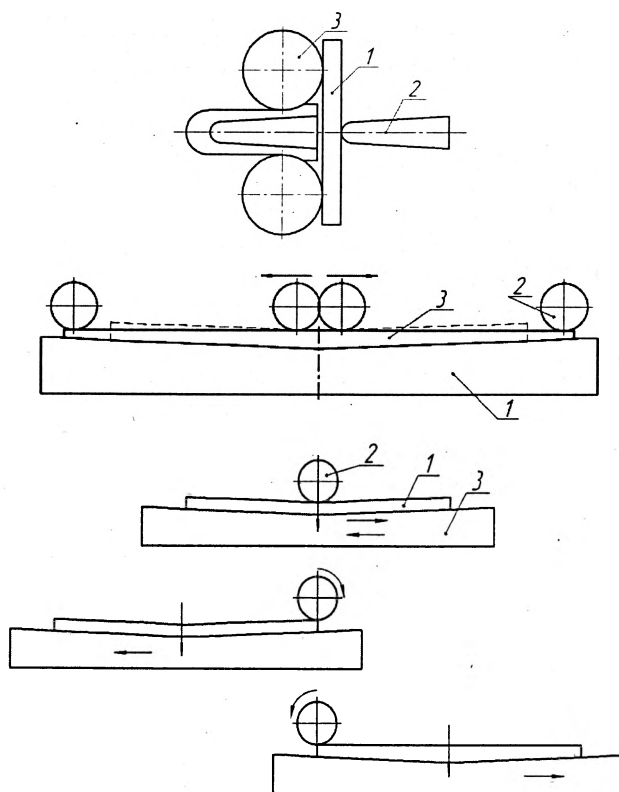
Схемы прокатки параболических заготовок малолистовых рессор неприводными валками
